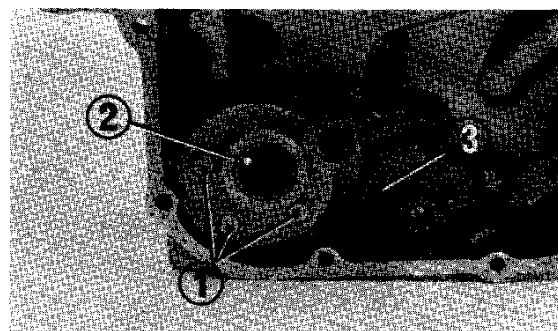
(1) Kühlwasserpumpe-Befestigungsschrauben
